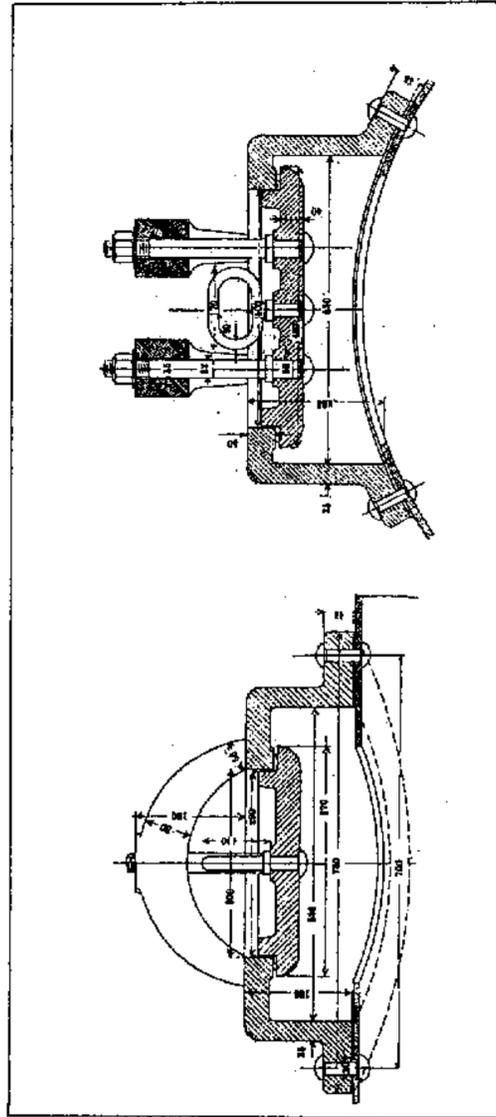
/1: Gusseisernes Mannloch, 30 x 40 cm lichte Weite (bestehend aus Rand, Deckel, Brücken, Haltegriff und Verschraubungen)
